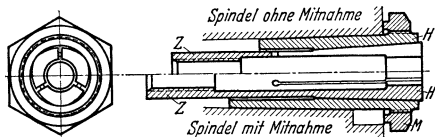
Einspannen von Fräsern mit zylindrischem Schaft.
